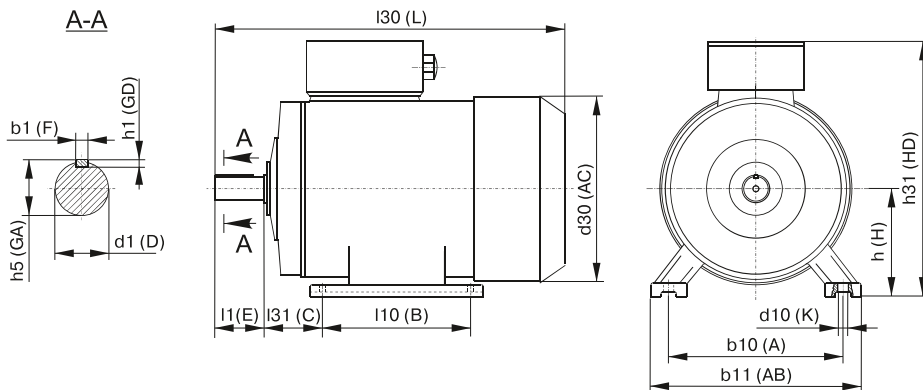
Размеры двигателей монтажного исполнения IM 1081 / Figure 1 – Motor dimensions of IM 1081 mounting version
